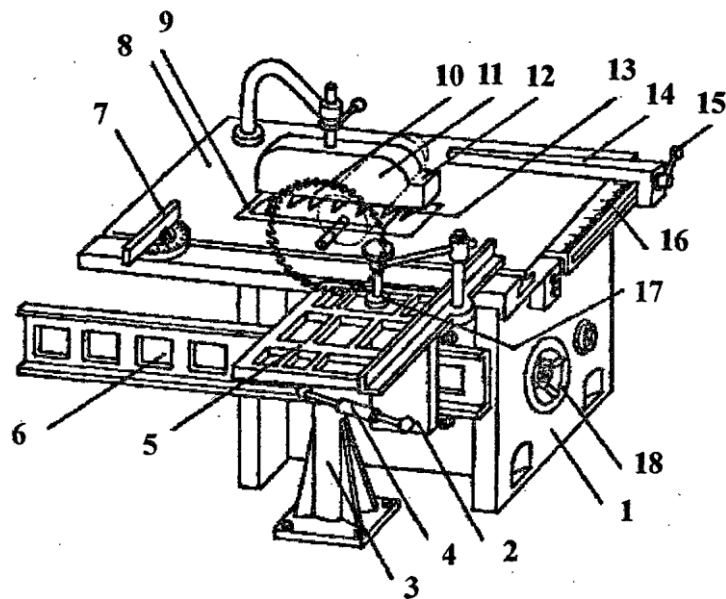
Універсальний круглопилочний верстат для змішаного розпилювання Ц6-2:
